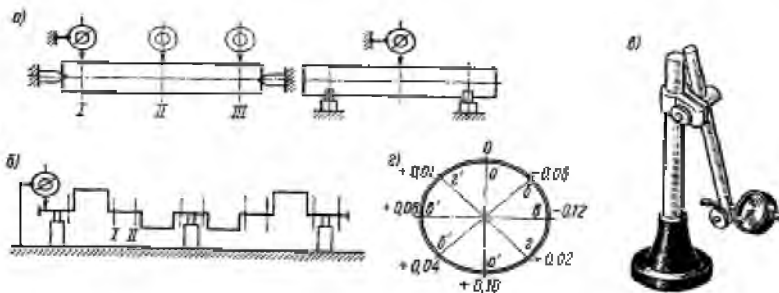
Схема перевірки прямолінійності циліндричного валу
